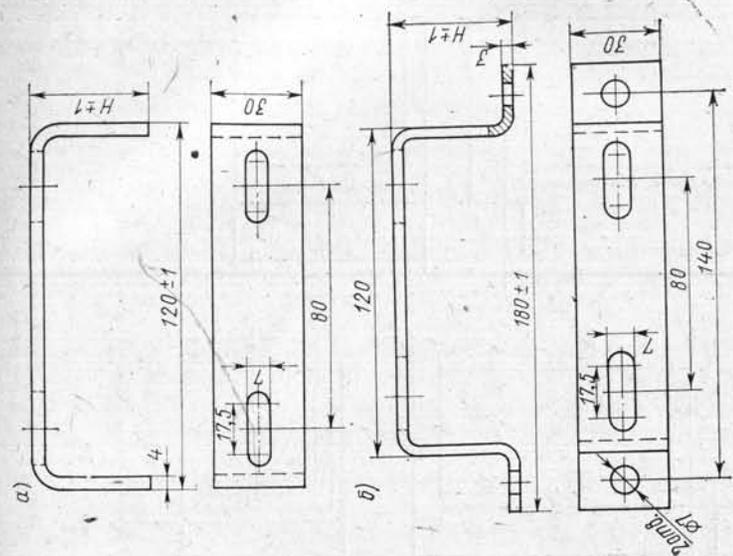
Мосты для крепления установочной арматуры: *а* — приварные с двумя перфорированными отверстиями; *б* — закрепляемые винтами, изготовляемые из легкого сплава.
